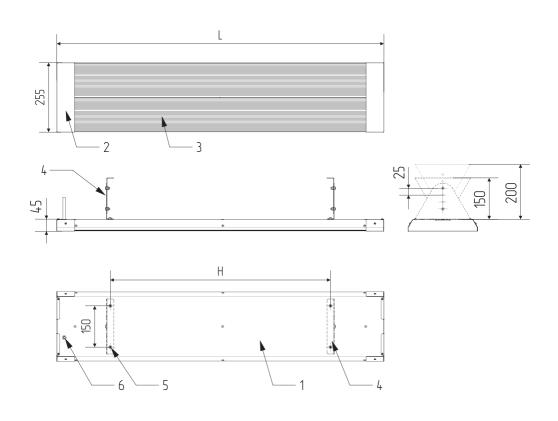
Внешний вид и элементы конструкции инфракрасного обогревателя.
